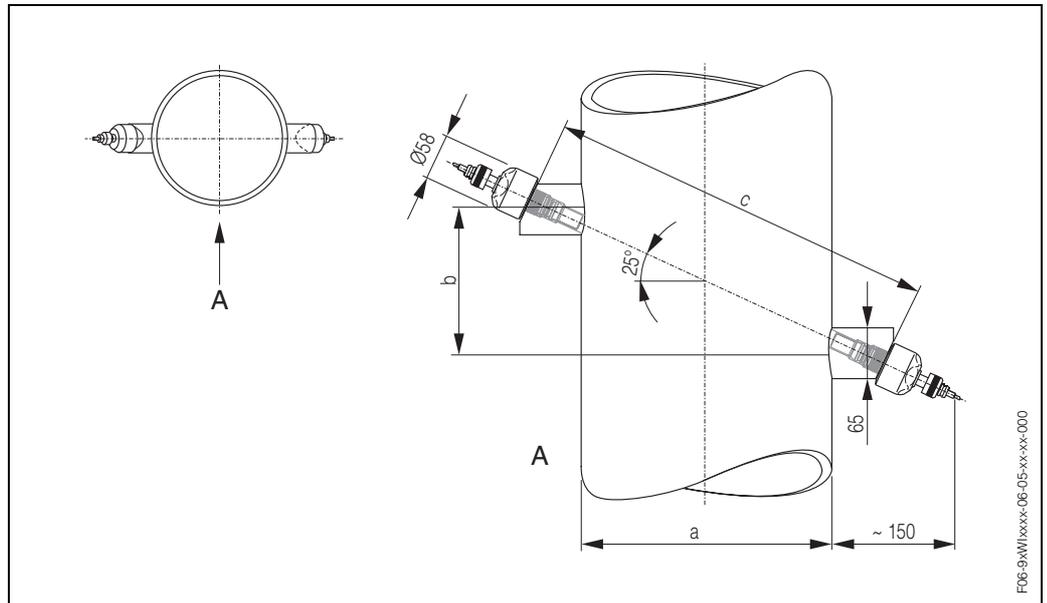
Dimensiones de los sensores W (versión de inserción)
